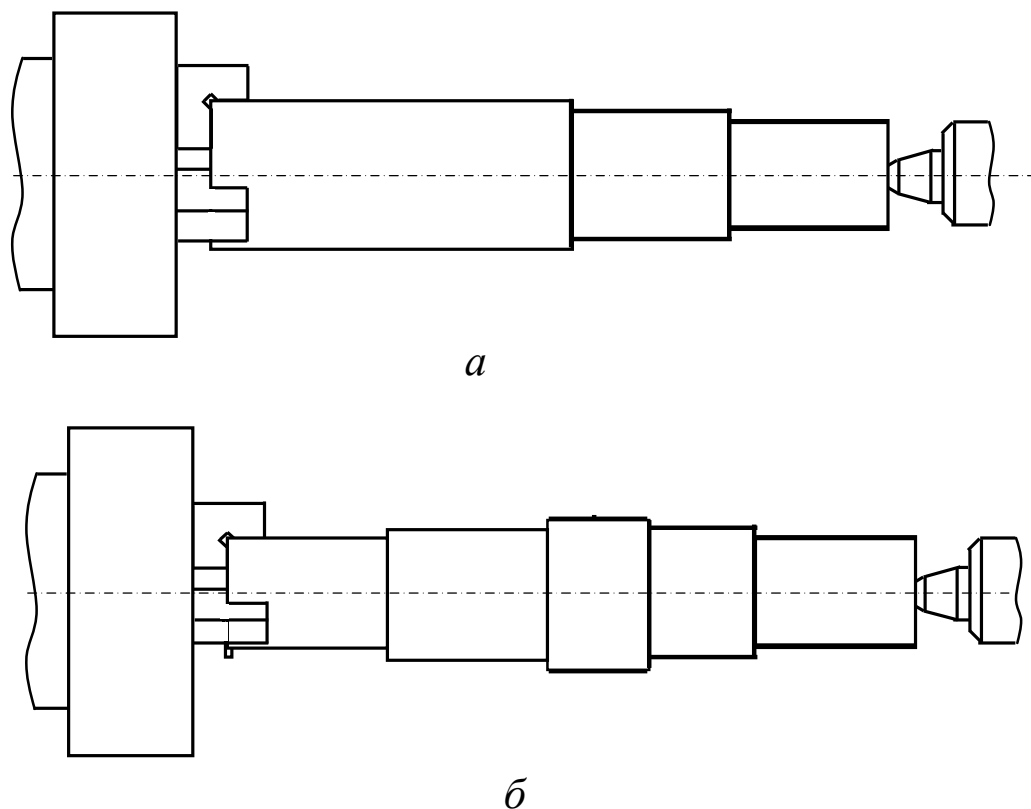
Послідовність попередньої обробки штучної заготовки з круглого прокату з використанням трикулачкового самоцентрувального патрона і обертового центра задньої бабки
